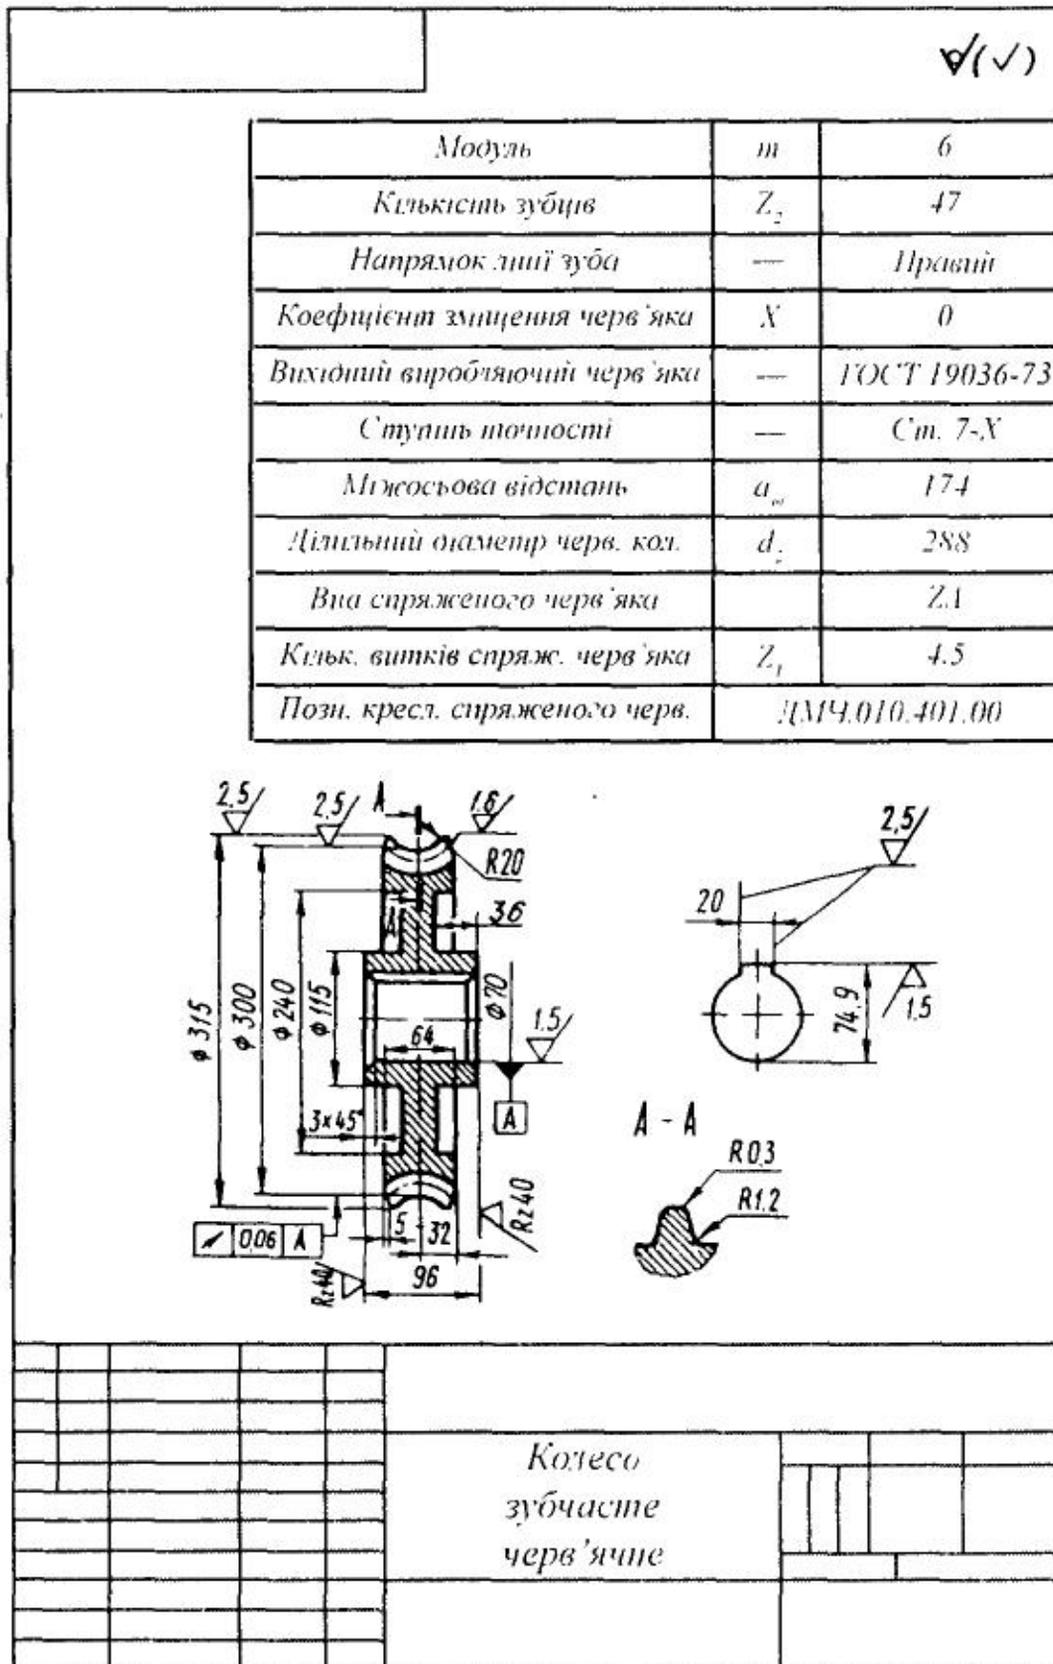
Креслення зубчастого черв'ячного колеса.
